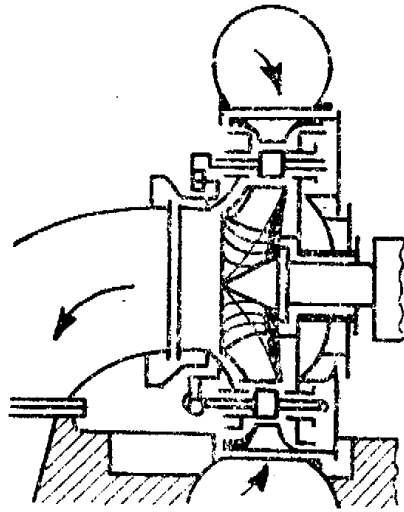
Turbină spirală orizontală cu carcasă spirală (melc)
